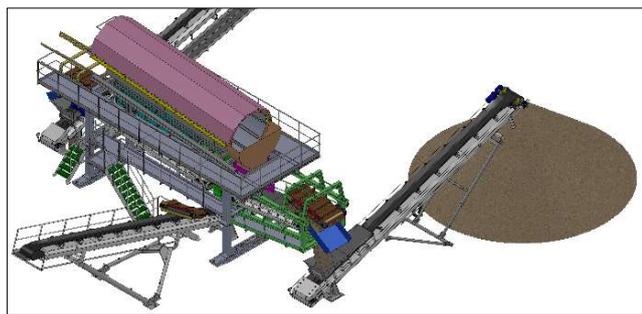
PLAN ET SCHEMAS DE L'INSTALLATION DE TRAITEMENT PRIMAIRE DES MACHEFERS
